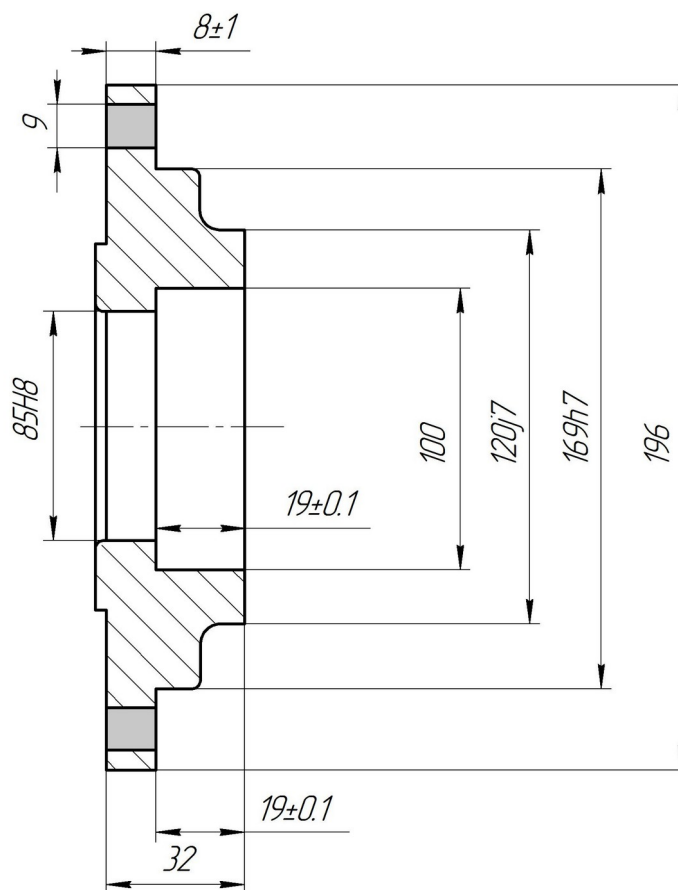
Заготовка стакану з призначеними припусками і допусками
